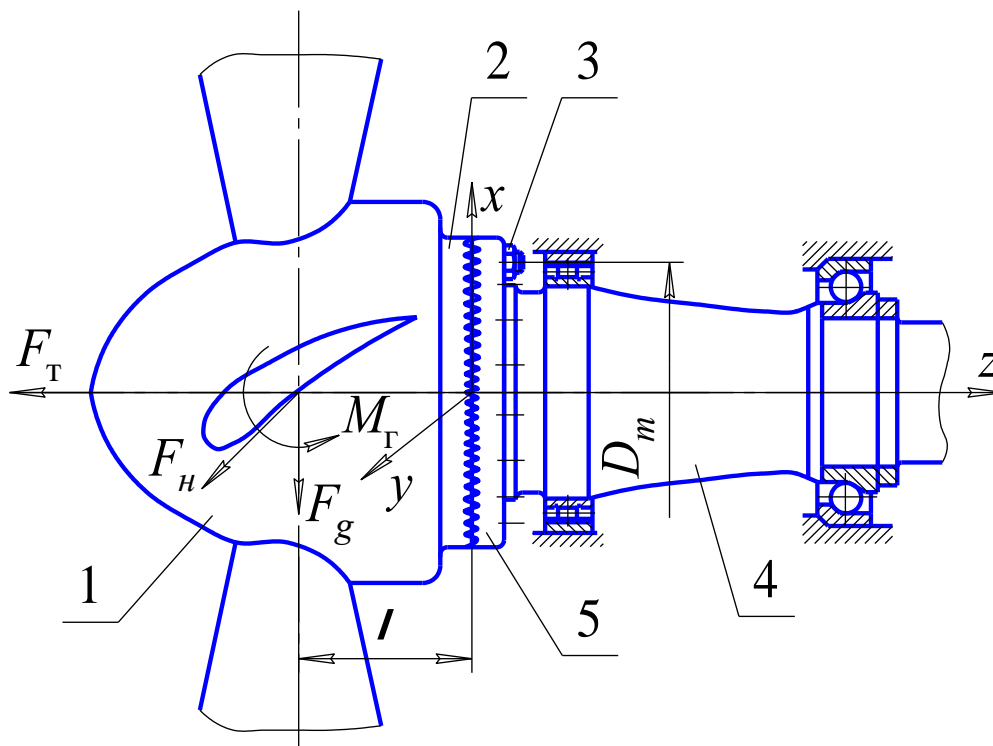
Фланец выходного вала хвостового редуктора МИ-4
